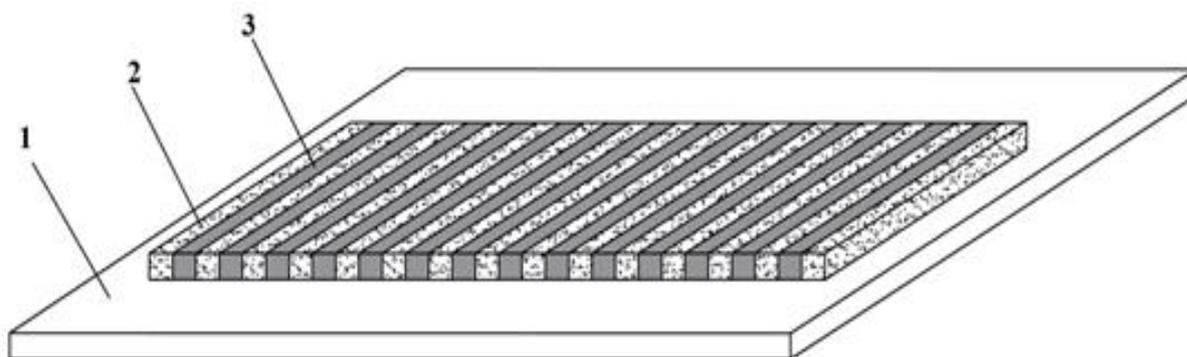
Блок магнитного рельса с вариантом сборки магнитов в пазы ферромагнитного зубчатого сердечника:
